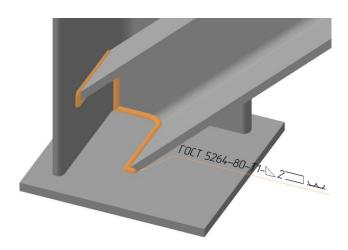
Пример конструкции выполненной в приложение «Каталог: сварные швы»
